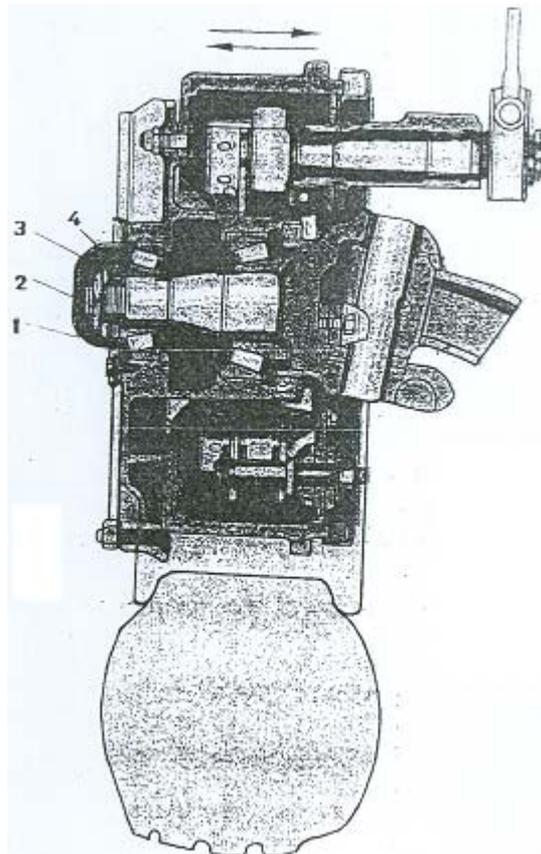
Проверка зазора между шкворнем и подшипником скольжения.
